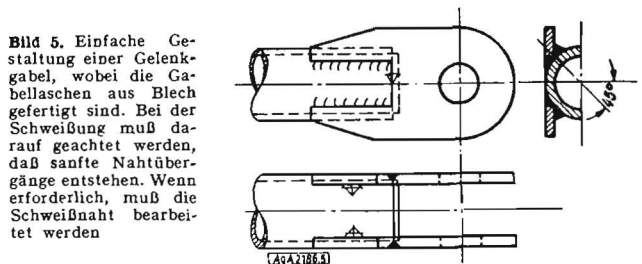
Einfache Gestaltung einer Gelenkgabel, wobei die Gabelaschen aus Blech gefertigt sind. Bei der Schweißung muß darauf geachtet werden, daß sanfte Nahtübergänge entstehen. Wenn erforderlich, muß die Schweißnaht bearbeitet werden
